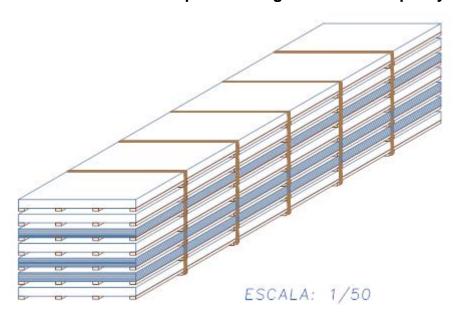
Ejemplo de embalaje para planchas de los dos tipos
